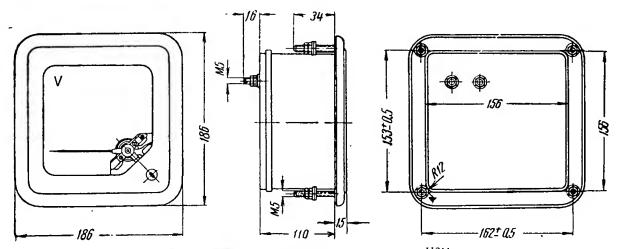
Габаритные размеры вольтметра типа Ц211 Fig. 1. Overall and installation dimensions of type Ц211 voltmeter
